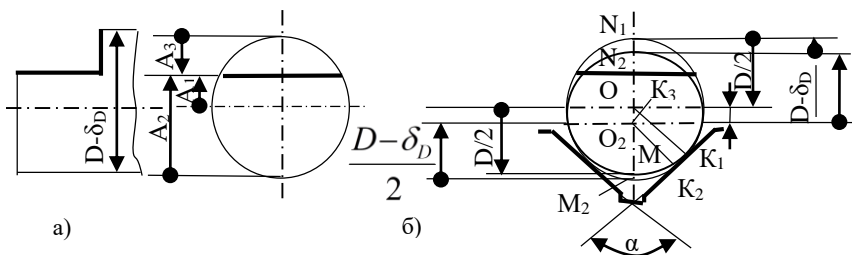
Схемы к определению погрешности установки цилиндрической заготовки на призме при различных схемах простановки операционного размера
